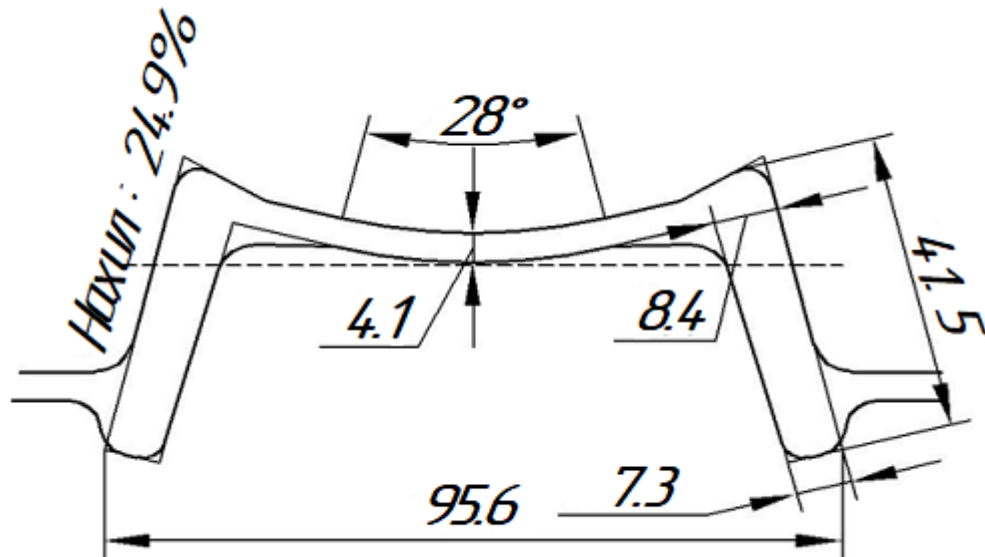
Ескиз передчистового калібра для прокатки швеллера №8
